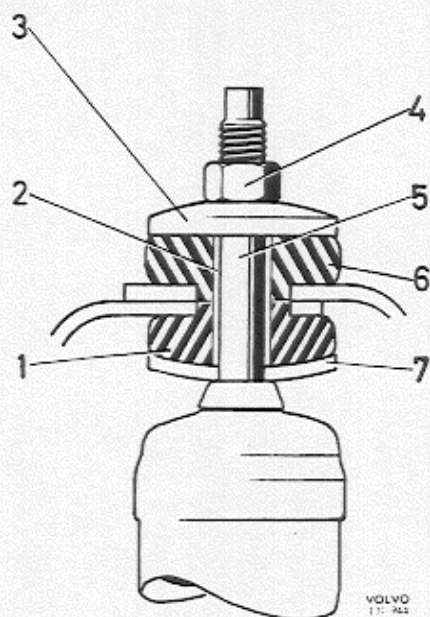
Vorderer Stoßdämpfer, obere Befestigung
